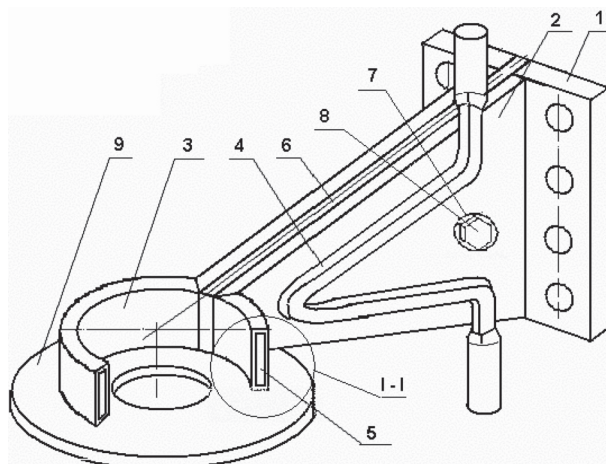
Индуктор для закалки ТВЧ: 1 – контактная колодка; 2 – токопередающие шины; 3 – индукционный виток; 4 – система охлаждения; 5 – система закалки (спрейер); 6 – система изоляции; 7 – крепежные изделия; 8 – дополнительное устройство
